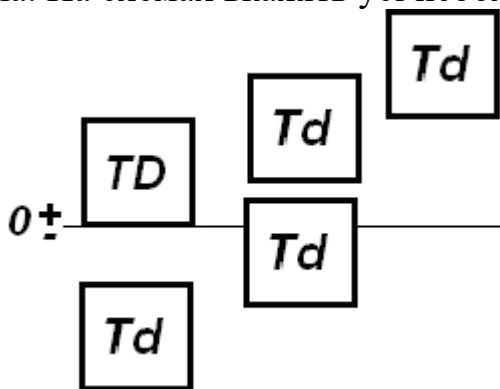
Схеми розташування полів допусків до задачі 43.
